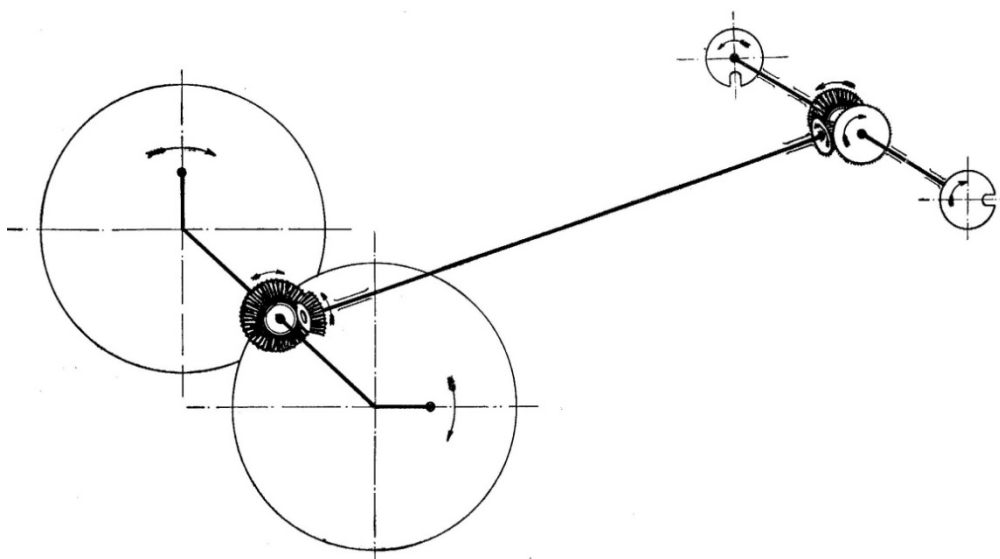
Esquema del accionamiento de la distribución Caprotti, mediante engranajes cónico.
